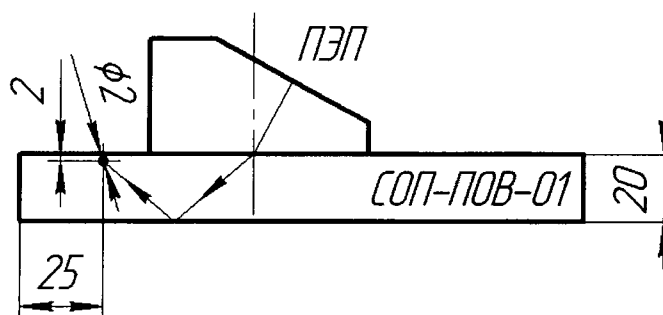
Установка акустического блока на поверхность СОП-ПОВ-01 для получения сигнала от бокового сверления диаметром 2 мм.
